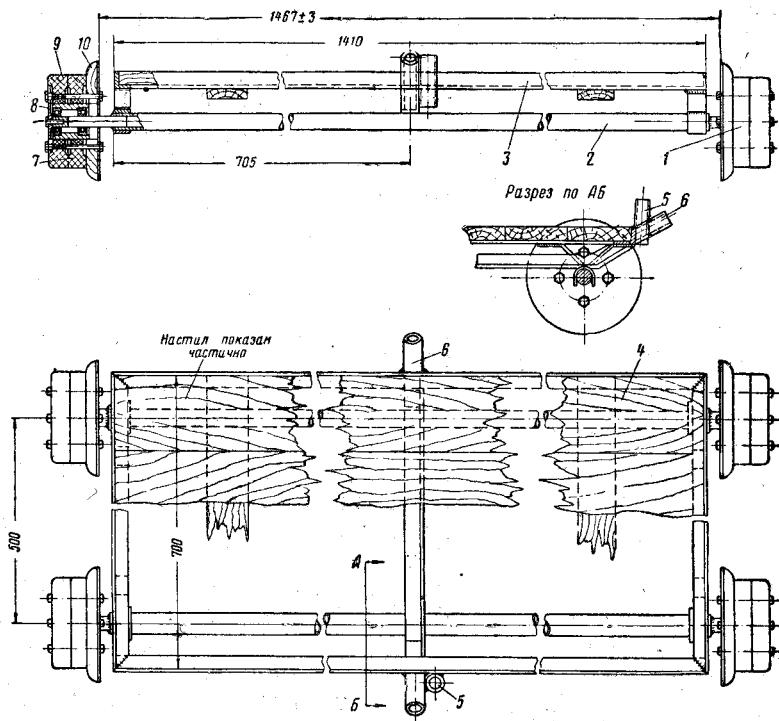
Тележка типа «метро» для перевозки инструмента:
